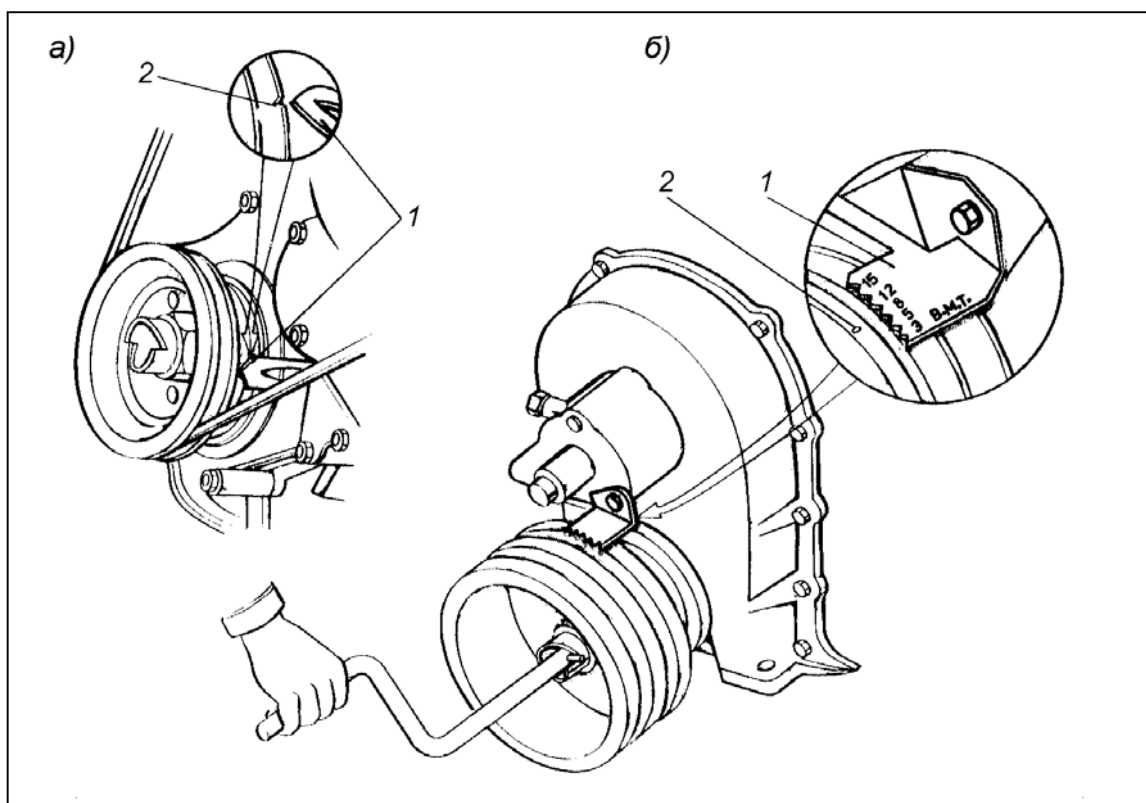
Положение коленчатого вала при установке привода распределителя зажигания:
